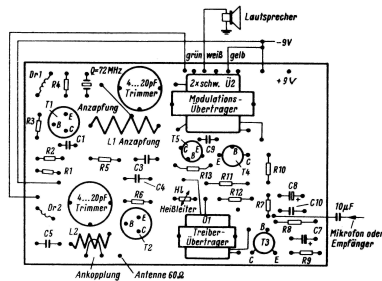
Bestückung der Druckplatte (in Draufsicht)
